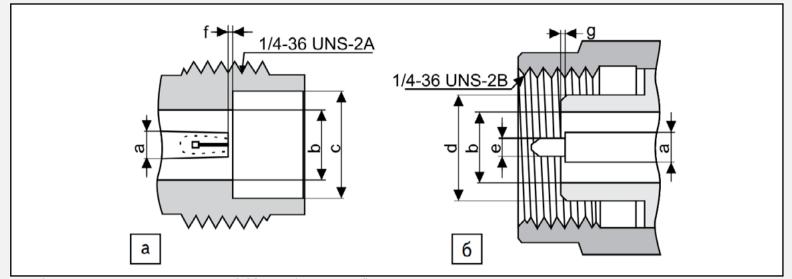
Интерфейс соединителя тип 2.92 мм: а) розетка; б) вилка
